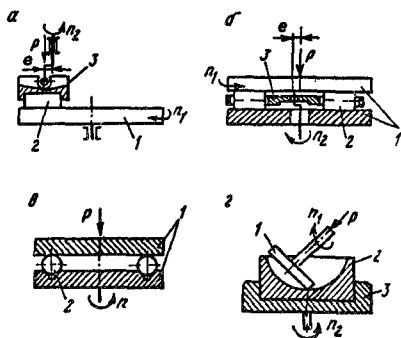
Схемы доводки плоских (а), цилиндрических (б) и сферических (в, г) поверхностей: 1 — притиры; 2 — обрабатываемые заготовки; 3 — держатели заготовок
